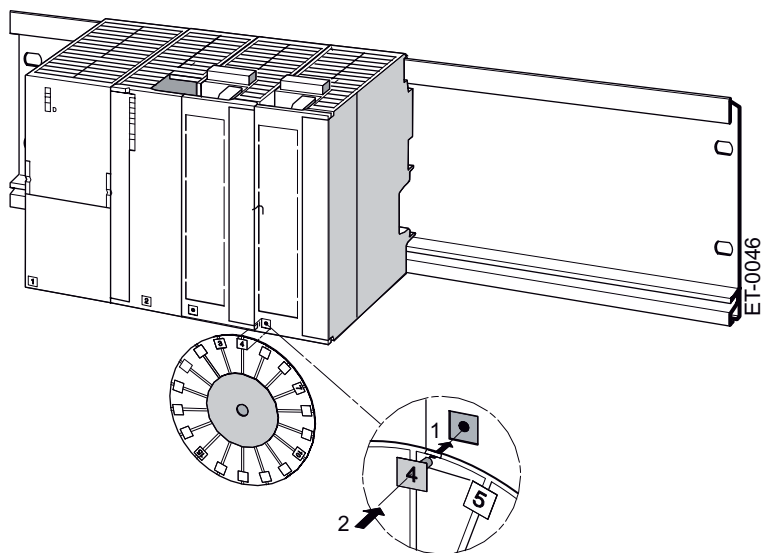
Steckplatznummern auf die Baugruppen stecken
